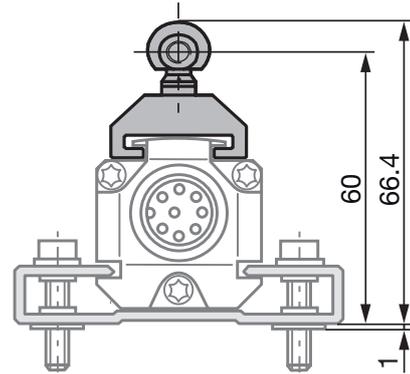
Maße und Abstände mit Positionsgewerber BTL5-F-2814-1S
